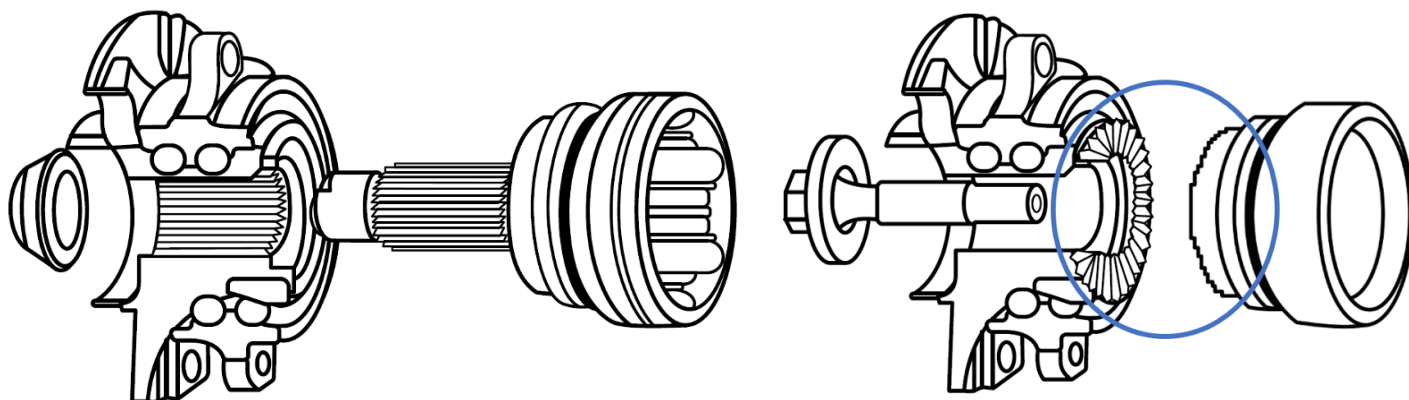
Ensemble de moyeu de roue à entraînement conventionnel (à gauche) et ensemble de moyeu de roue à cannelures axiales (à droite). Noter que les cannelures apparaissent comme des dents d'engrenage cylindrique à la fois du côté du moyeu et de l'arbre de roue (encerclé).
